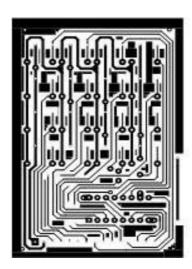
Diseño de Pistas de Tarjeta del Teclado
